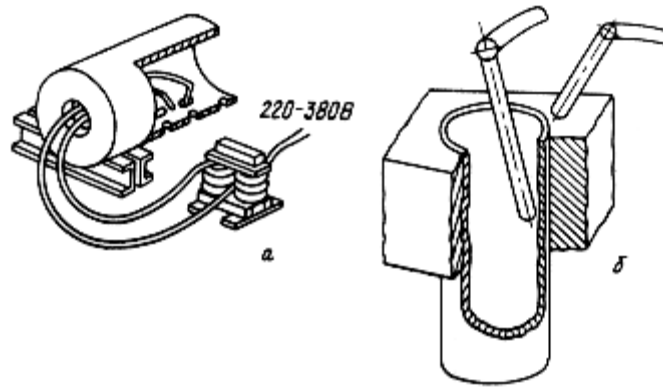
Магнитопорошковая дефектоскопия барабана с вальцованными трубами: а - схема установки; б - способ намагничивания металла барабана
